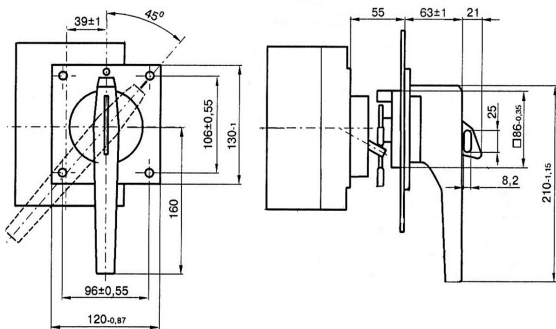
Расположение отверстий для крепления ручного дистанционного привода
